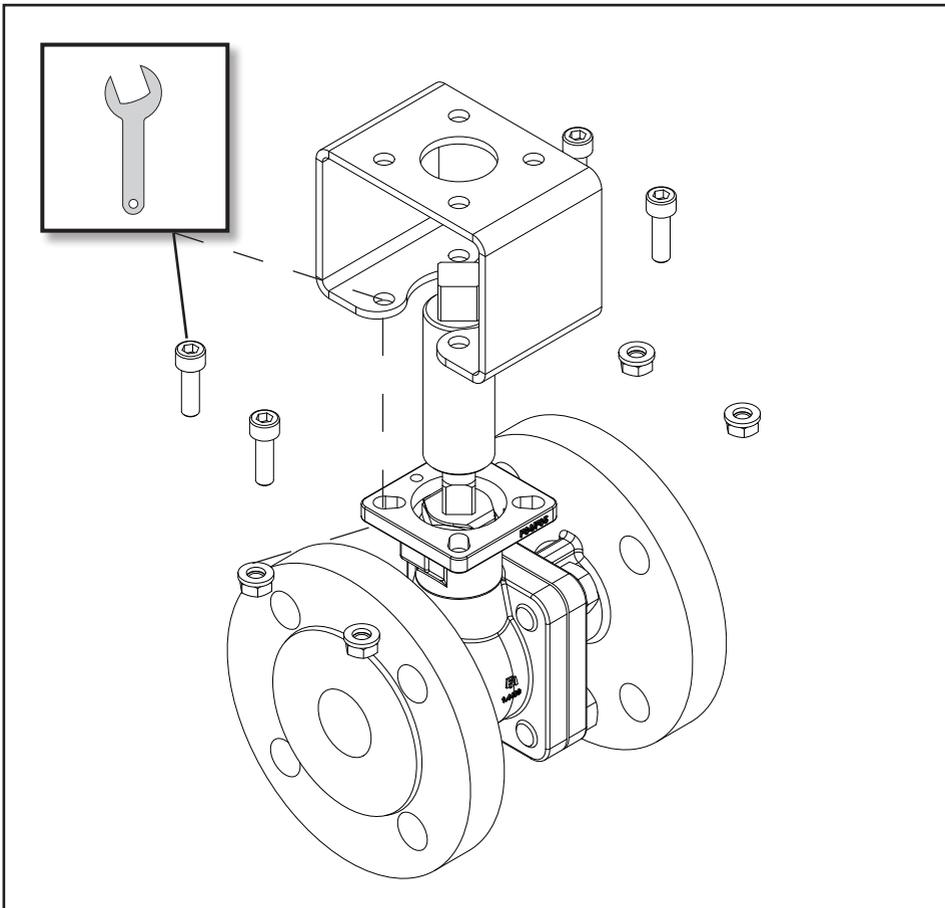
Montage / Demontage, Montage mittels Konsole und Spindel
